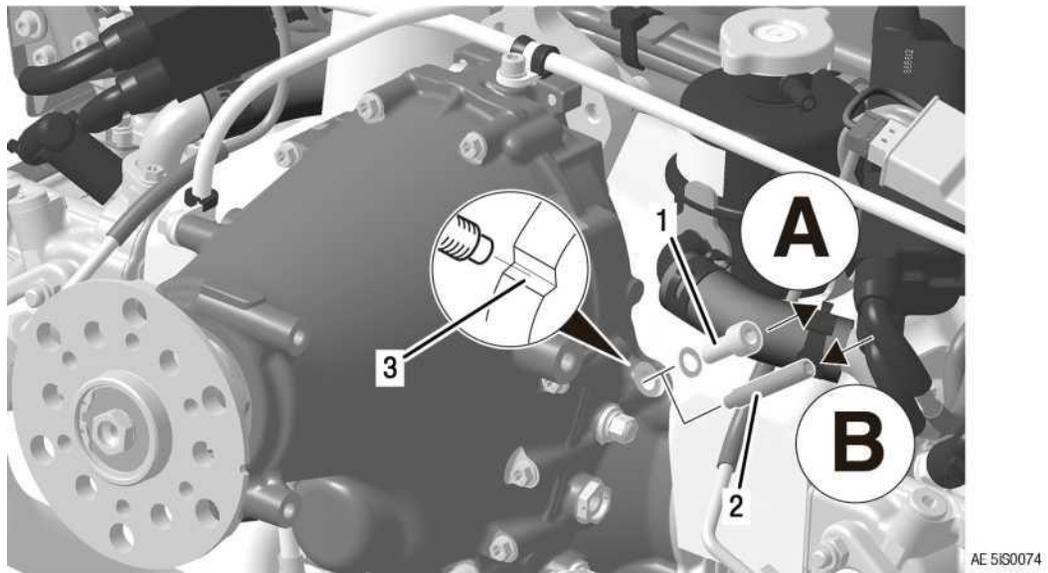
Стопорение/расстопорение коленвала ТИПОВОЙ РИСУНОК
